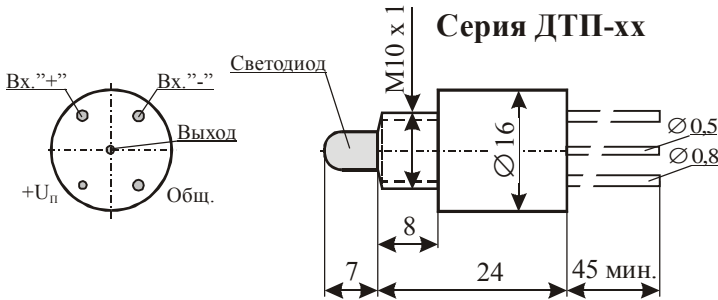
а Внешний вид и габаритные размеры датчиков тока серии ДТП
